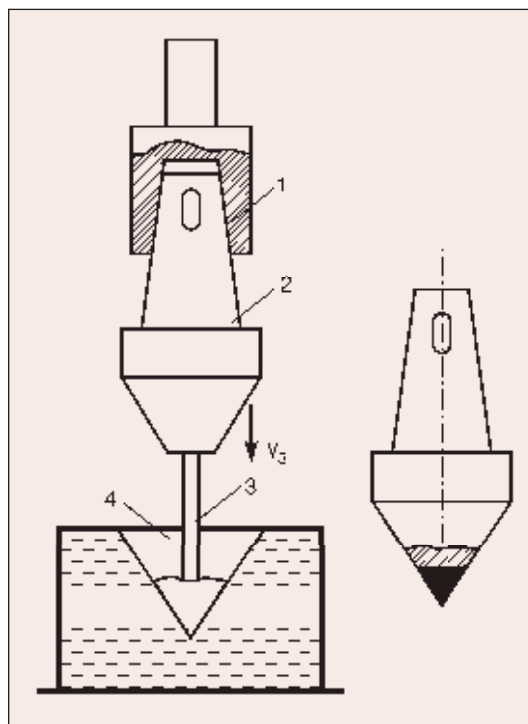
Схема стыкошлаковой наплавки: 1 — плавящийся электрод; 2 — патрон для закрепления детали; 3 — наплавляемый керн; 4 — кристаллизатор
